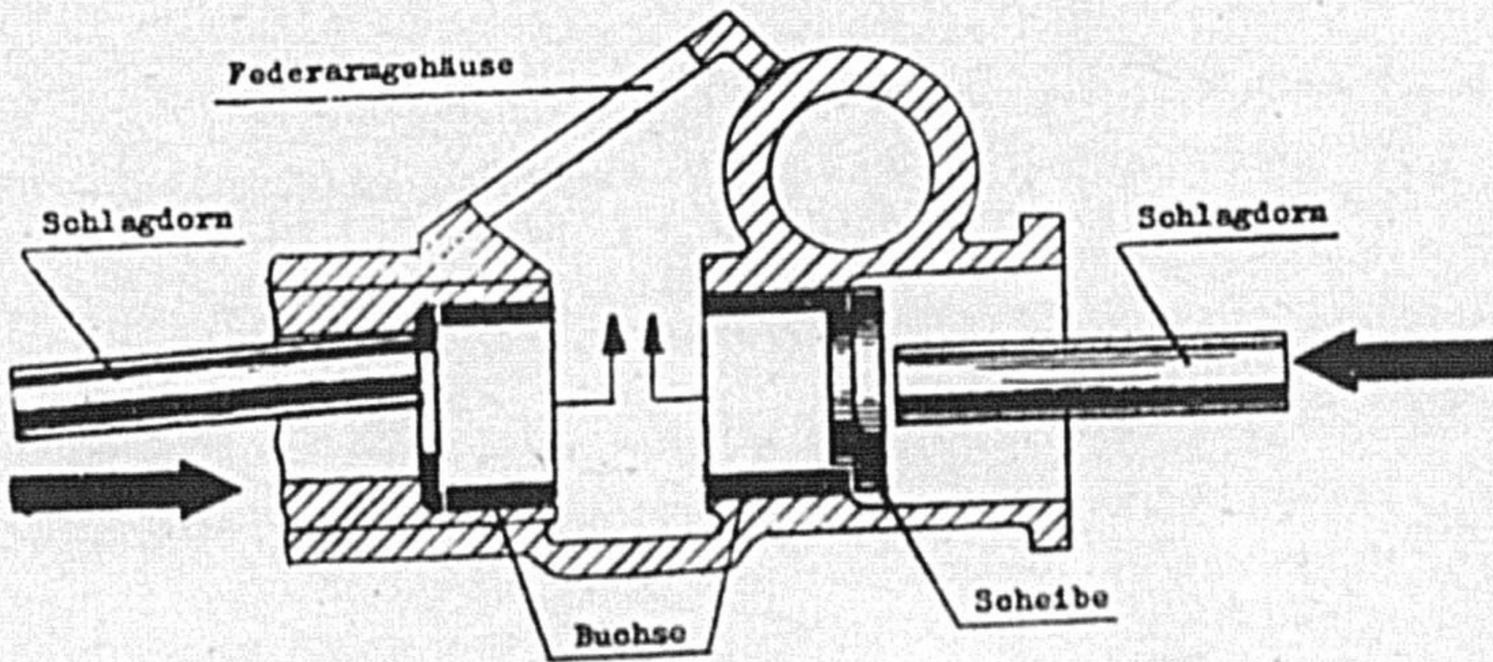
Ausbau der Bronzebuchsen im Federarmgehäuse
